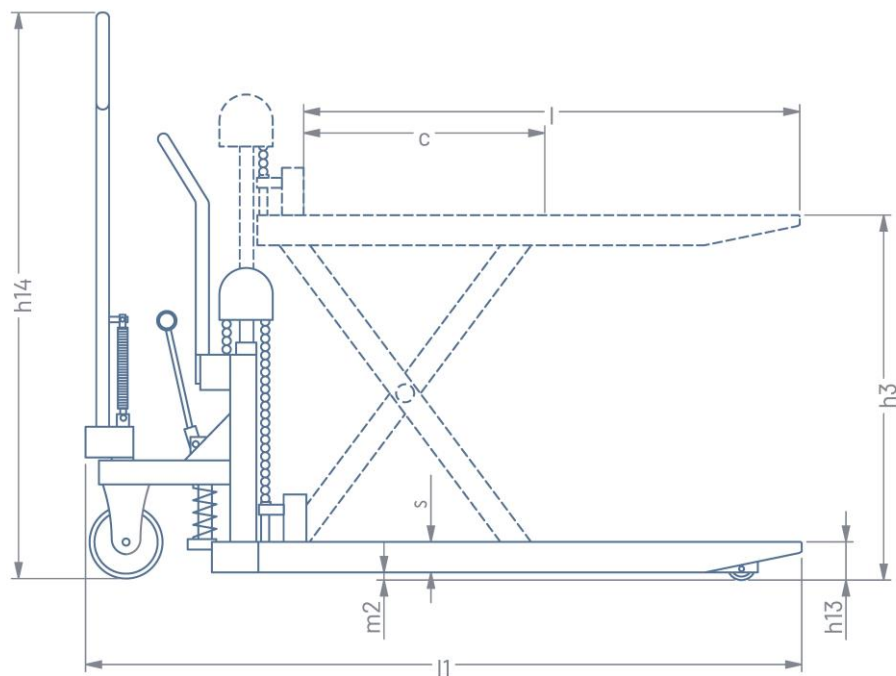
ZAC-GO Seitenansicht mit Kürzeln
